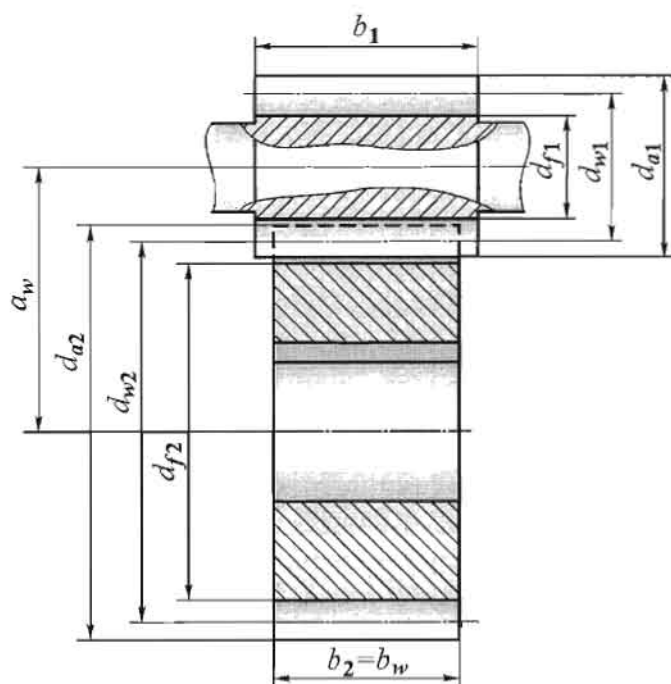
Геометрические параметры цилиндрической зубчатой передачи
